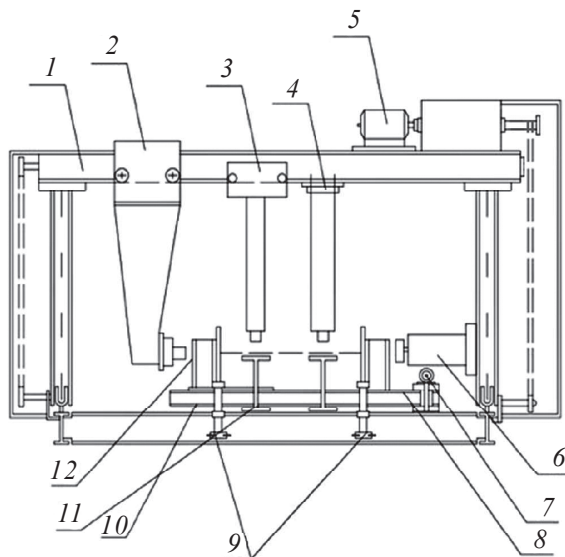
Установка с передвижным порталом для сборки стержней двутаврового сечения:
